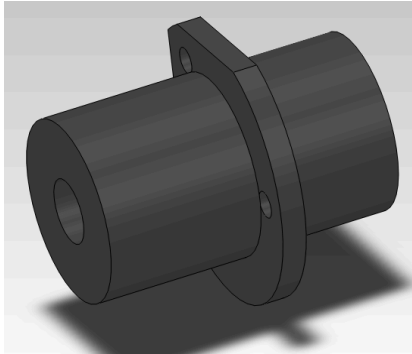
Primeiro método de fabricação por soldagem a arco.
